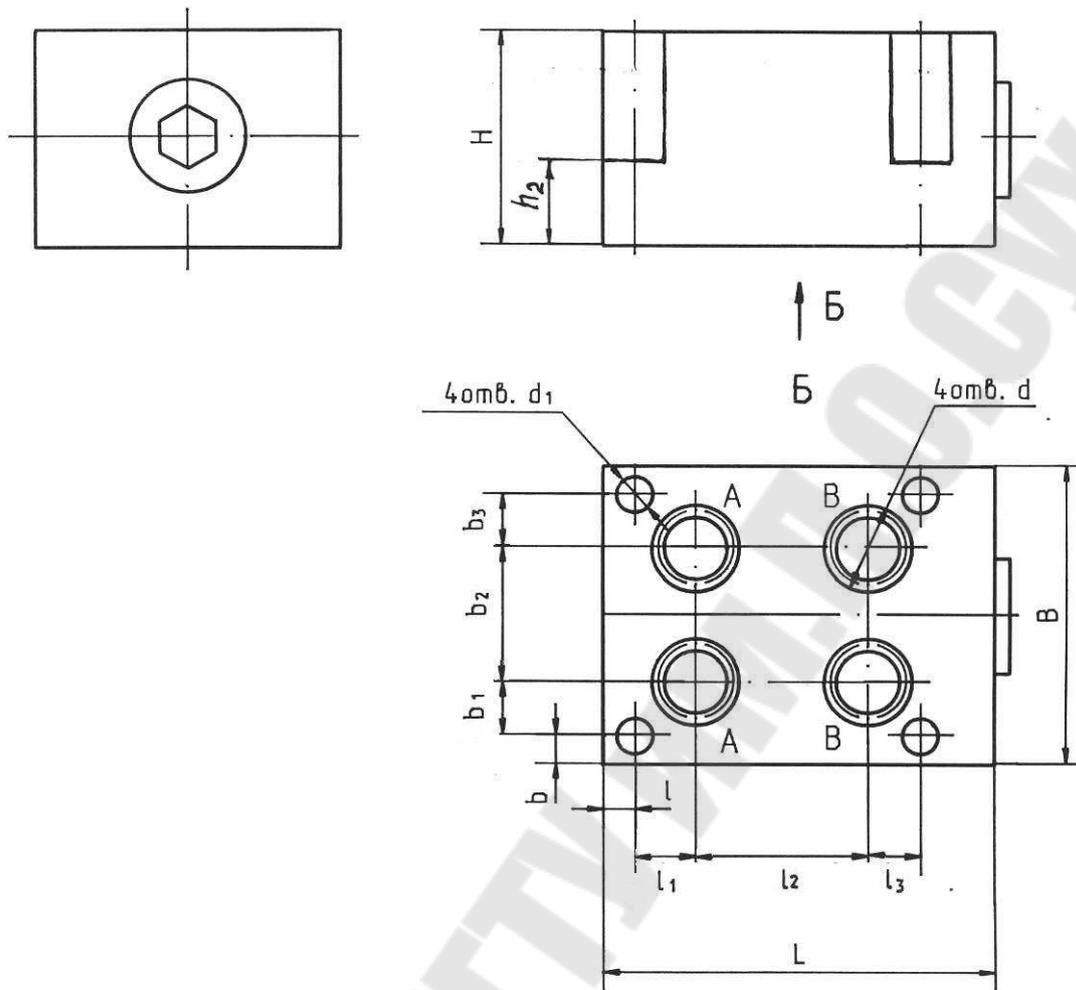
Общий вид блока присоединительного клапана обратного БПВ – 6. КО
